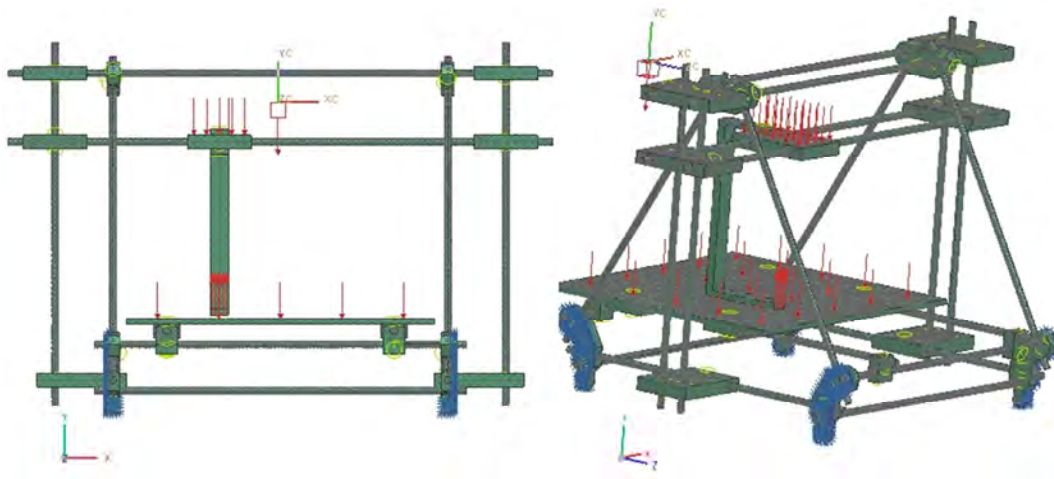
Restricciones y cargas aplicadas a la estructura de la máquina de electroerosión.
